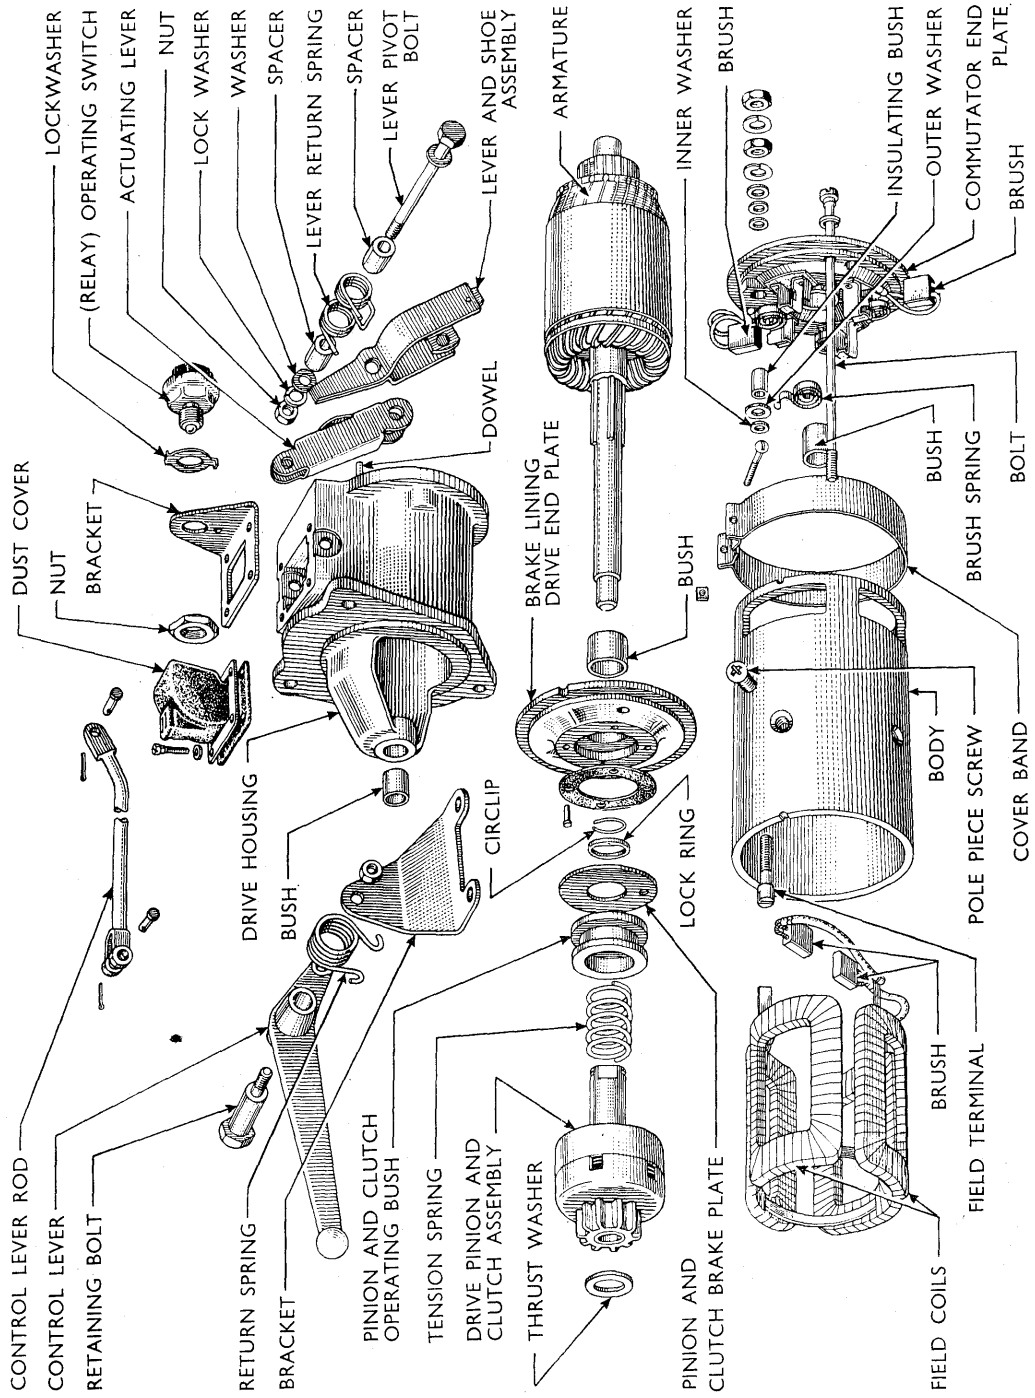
Startmotoren i exploded-view. (Se forklaring på side 40).
